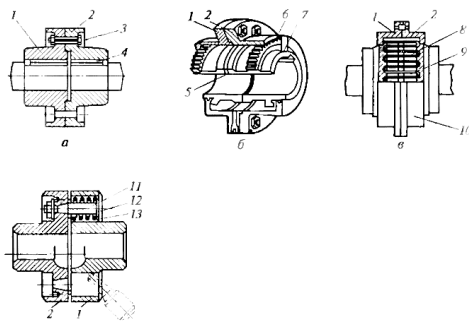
Соединение валов с помощью муфт: а — жесткой поперечно-свертной; б — зубчатой; в — полужесткой зубчато-пружинной; г — упругой втулочно-пальцевой; 1 и 2 — полумуфты; 3 — точеный болт; 4 — шпонка; 5 и 7 — ступицы; 6 — зубчатый венец; 8 — ленточная пружина; 9 — зубья; 10 — кожух; 11 — палец-болт; 12 — кожаная шайба; 13 — разрезное кольцо
